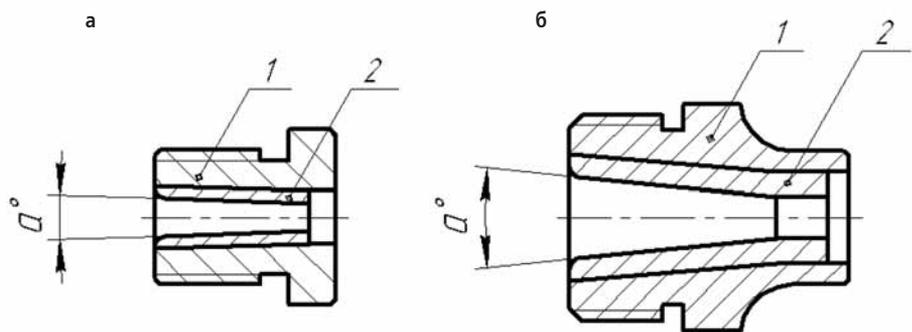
Форсунка в сборе: а – форсунка для технологии Jet1; б – форсунка для технологии Jet2; 1 – корпус; 2 – втулка из твердого сплава
